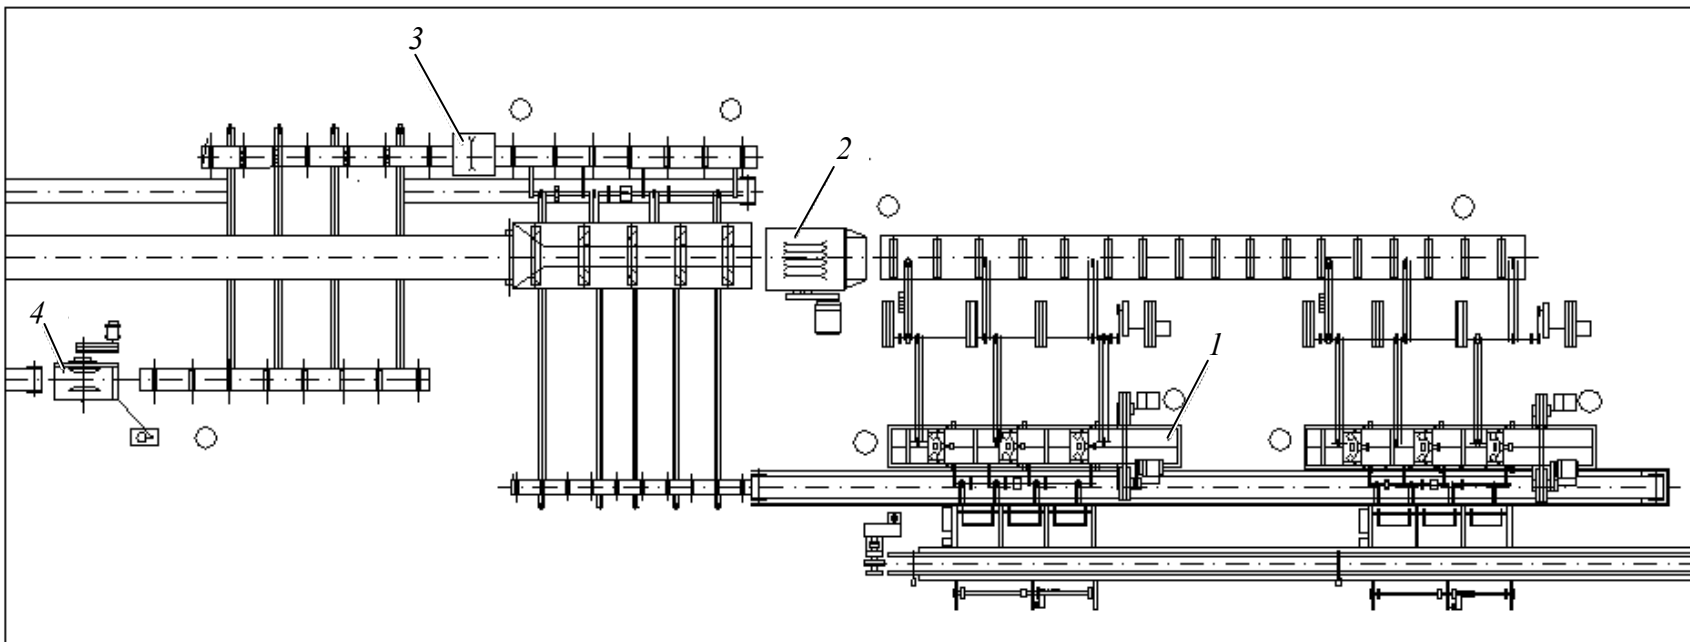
Схема расположения оборудования в цехе на базе горизонтальных ленточнопильных и круглопильных станков:
